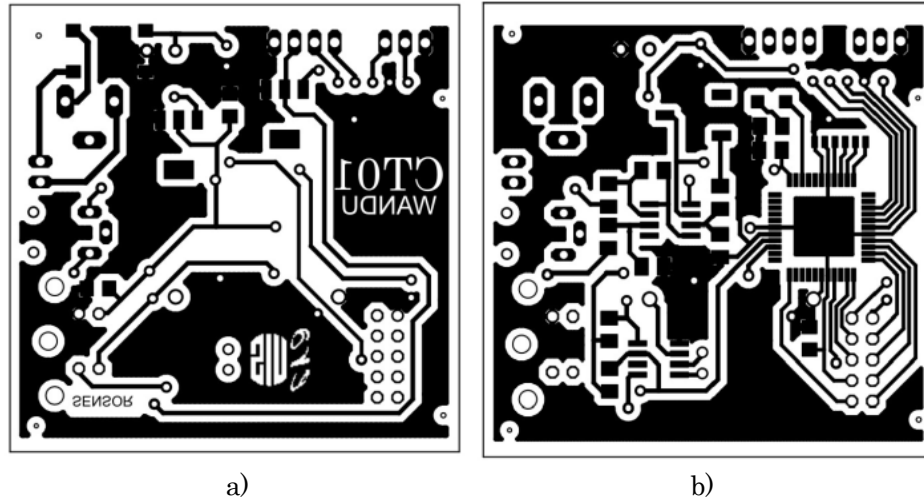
, PCB de la tarjeta de control del CT01. a) Bottom. b) Top.
